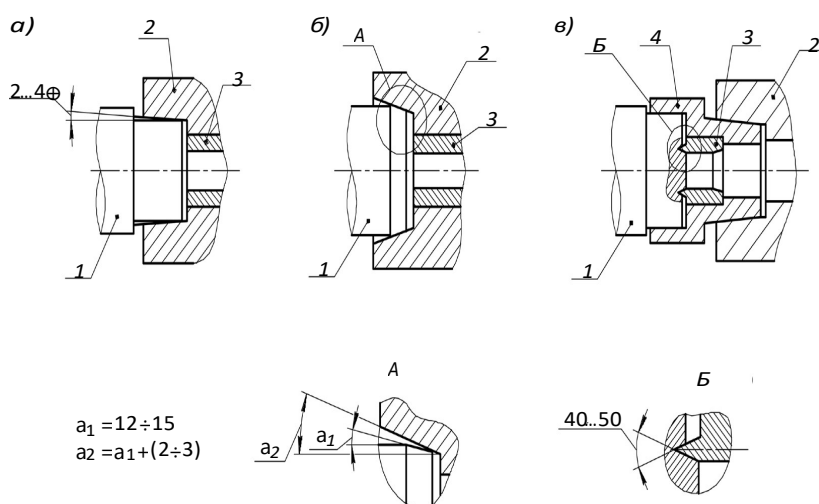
Узлы базирования заготовки: а – с помощью конической поверхности малой конусности; б – с помощью короткой конической фаски; в – с помощью переходной втулки; 1 – заготовка; 2 – шпindelь маслоприемника; 3 – кондукторная втулка; 4 – переходная втулка
